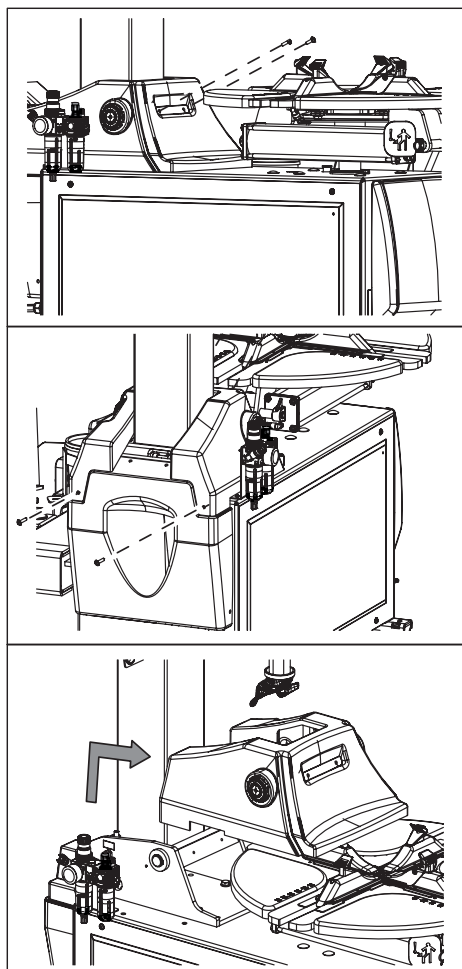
Retiro de la cubierta de plástico del pie de la columna
